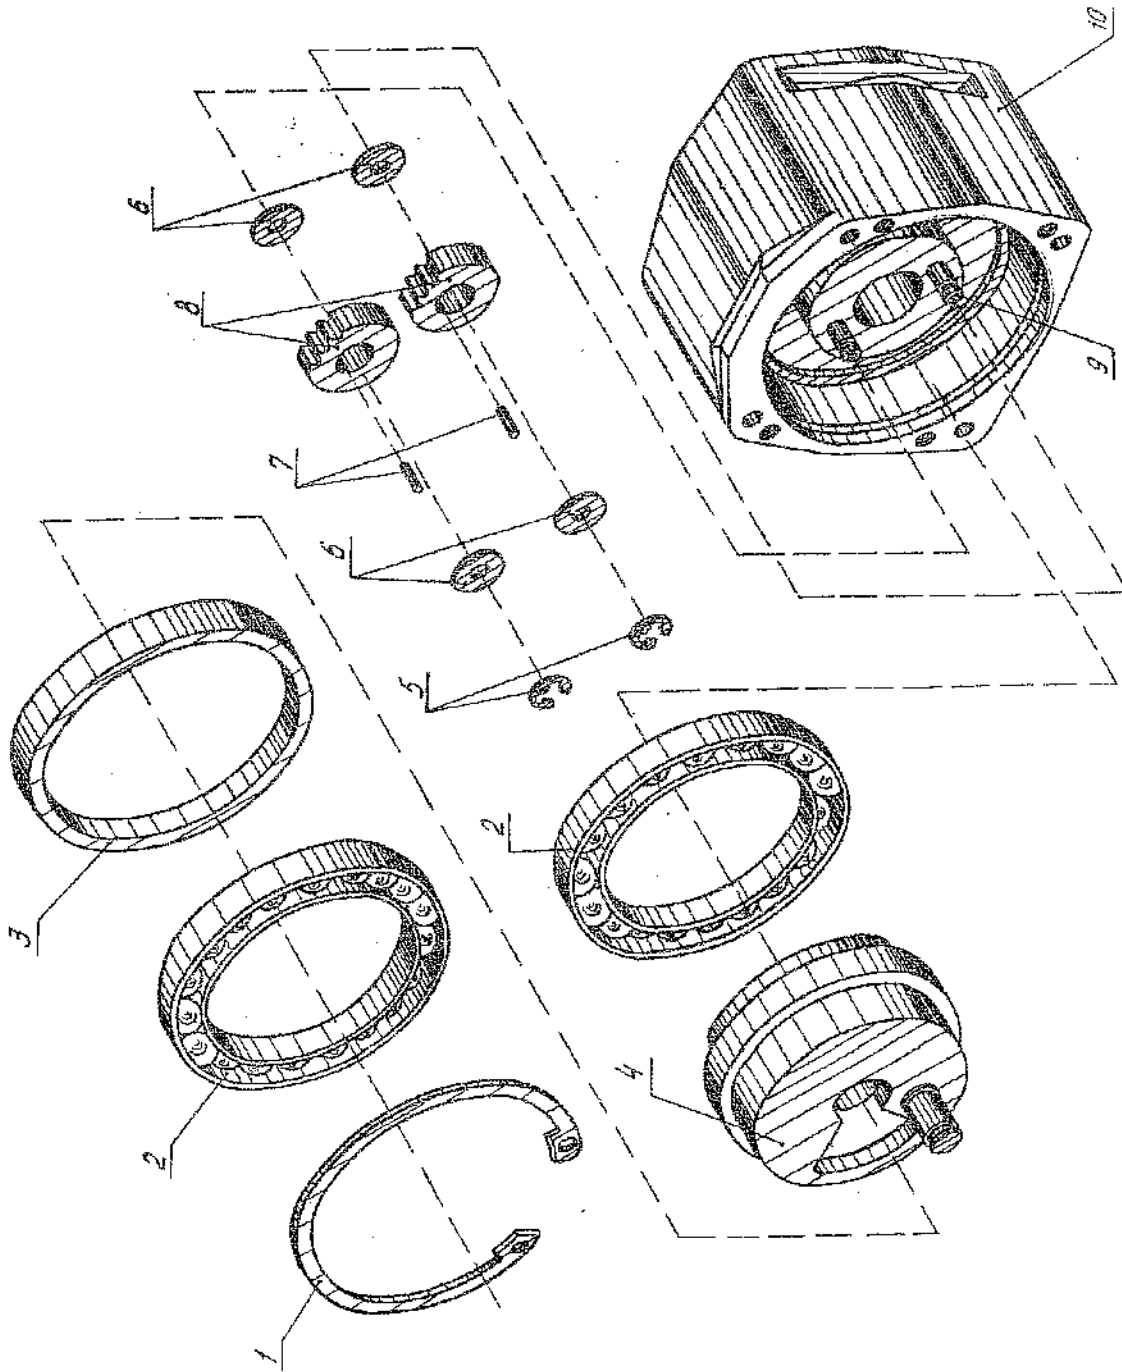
Сборка щита промежуточного с шариковыми подшипниками
